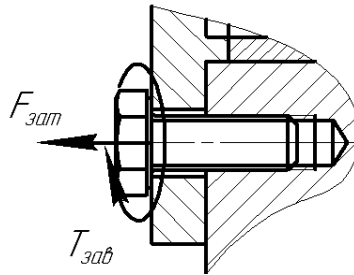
Соединение крышки подшипника с корпусом
